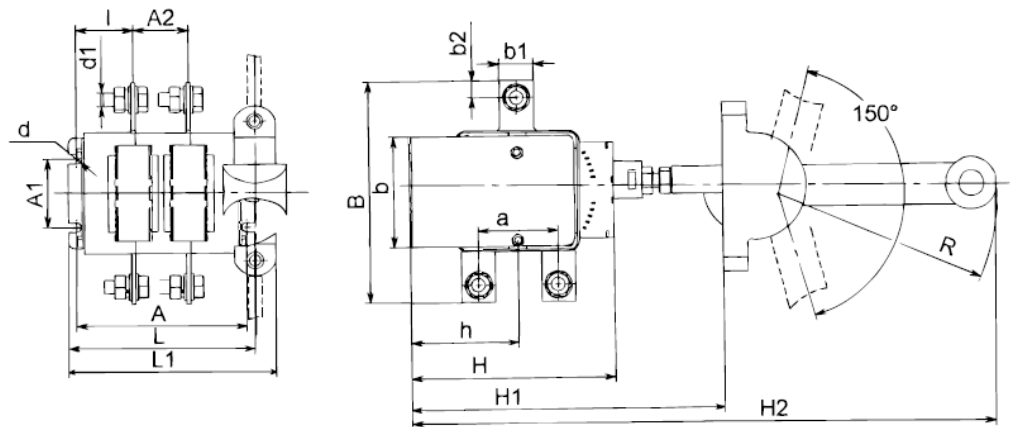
Выключатель-разъединитель двухполюсный на два направления с передней смещенной рукояткой.
